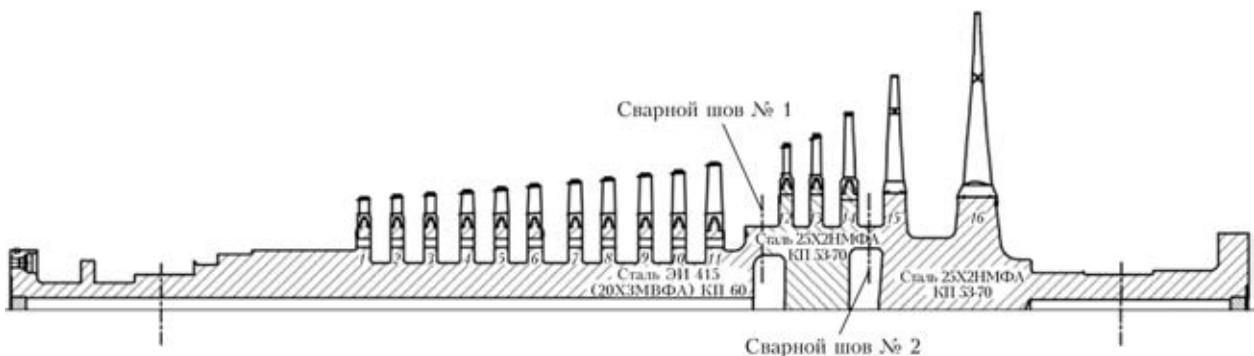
Эскиз продольного сечения сварного ротора ЦСД турбины мощностью 325 МВт
